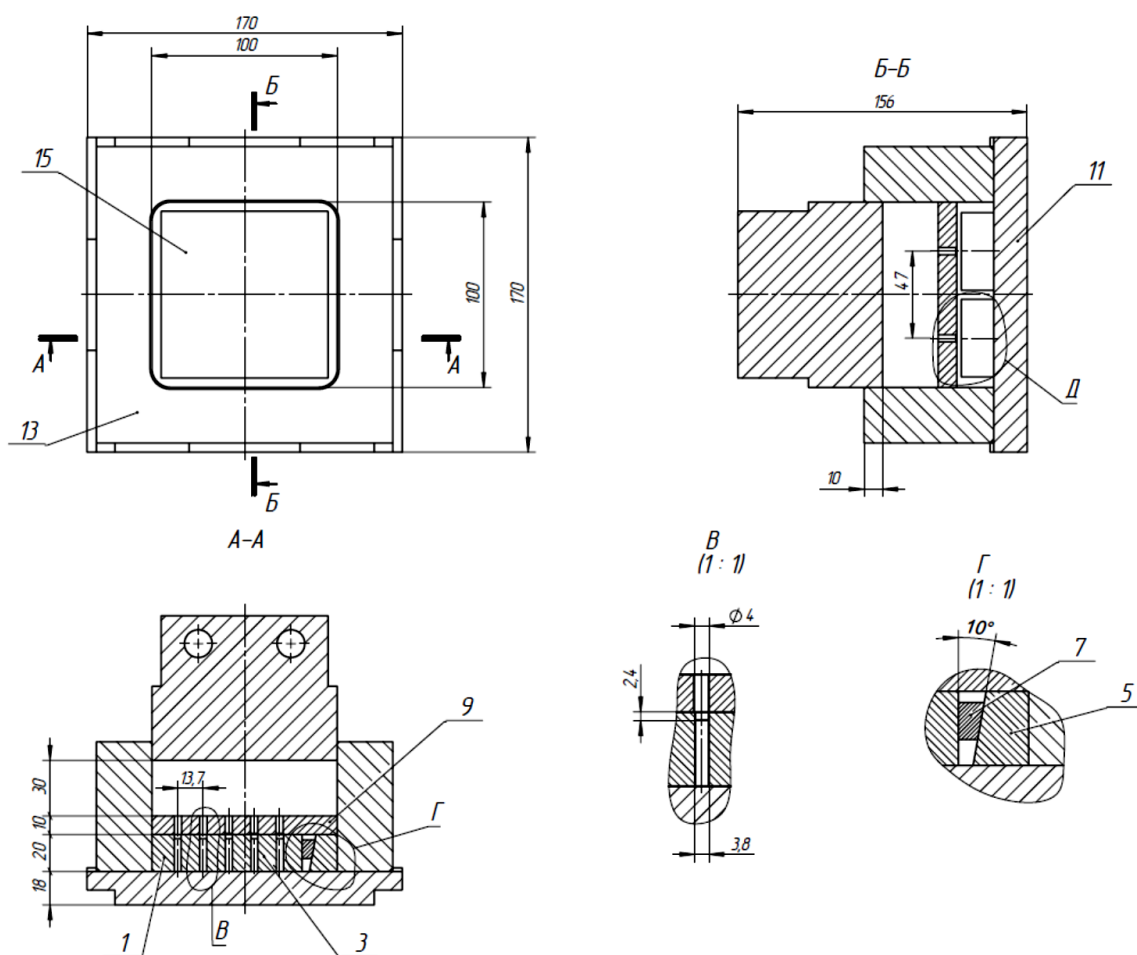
Чертеж технологической оснастки для пропитки заготовок
